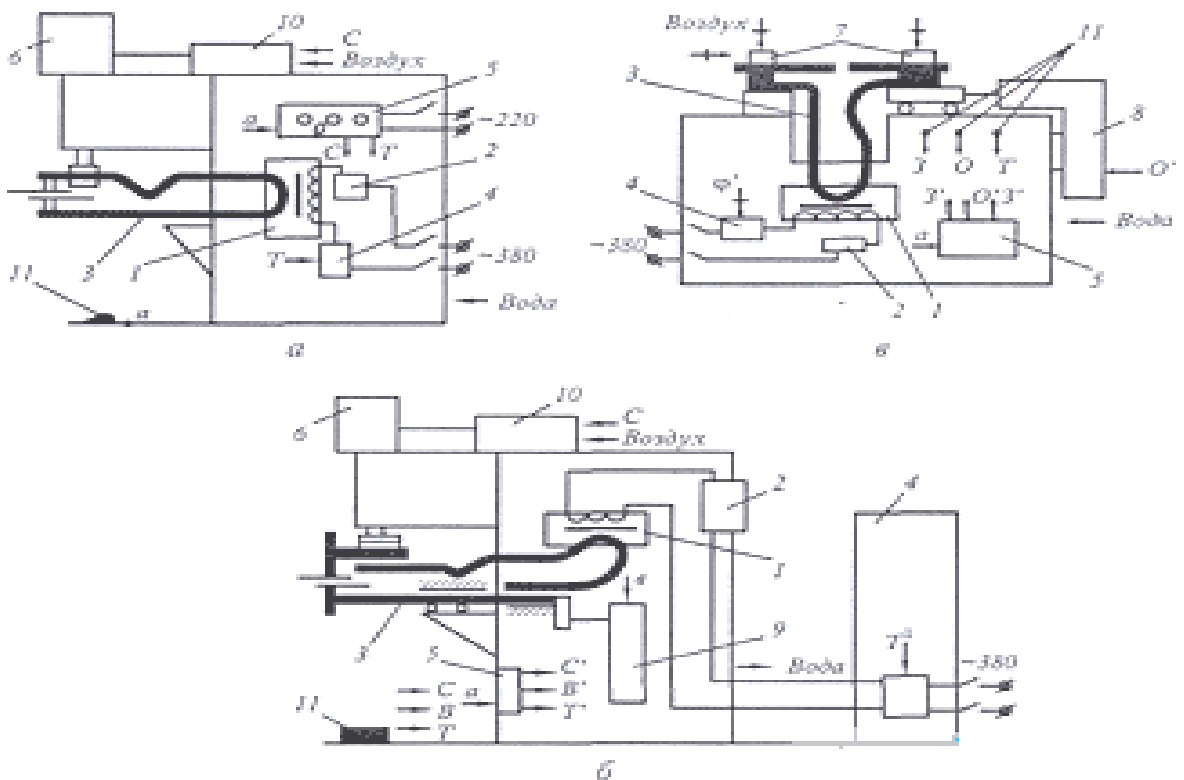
Типовые схемы машин для контактной точечной (а), шовной (б) и стыковой (в) сварки: 1 - трансформатор; 2 - переключатель ступеней; 3 - вторичный сварочный контур; 4 - прерыватель первичной цепи; 5 - регулятор; 6 - привод сжатия; 7 - привод зажатия деталей; 8 - привод осадки деталей; 9 - привод вращения роликов; 10 - аппаратура подготовки; 11 - орган включения
